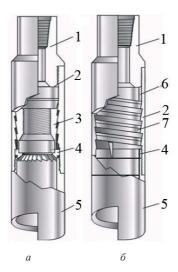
Овершот: *а* – с цанговым захватом; *б* – со спиральным захватом; 1 – верхний переходник; 2 – корпус; 3 – цанговый захват; 4 – ограничительное кольцо; 5 – направляющая воронка; 6 – пакер; 7 – спиральный захват
